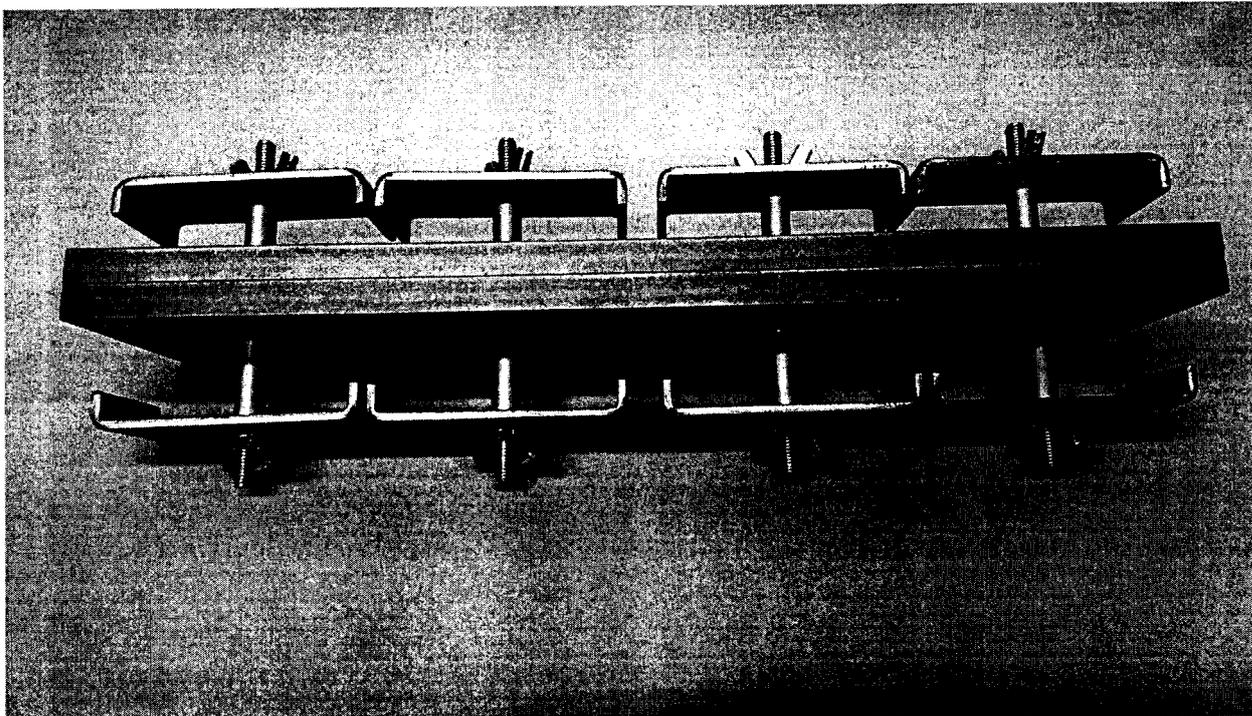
Пластина для размещения датчиков ДТР (чертёж № ИН7.450.000.910)
